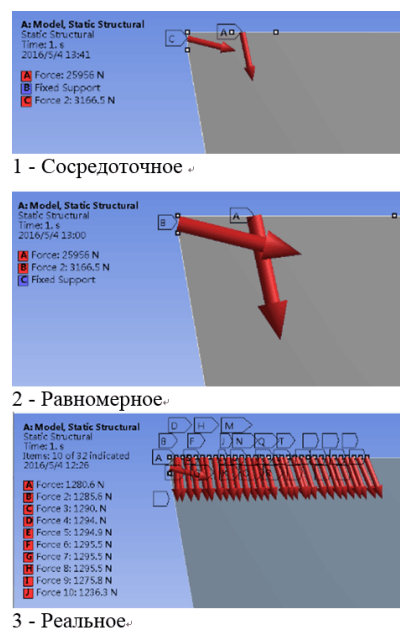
Виды приложения контактных нагрузок на поверхностях режущей пластины
